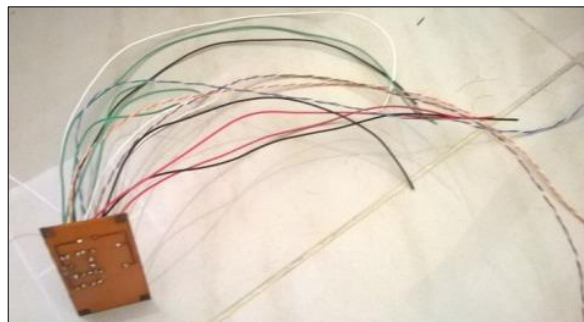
PLACA DE BAQUELITA CON LOS CABLES DE COBRE SOLDADOS.
